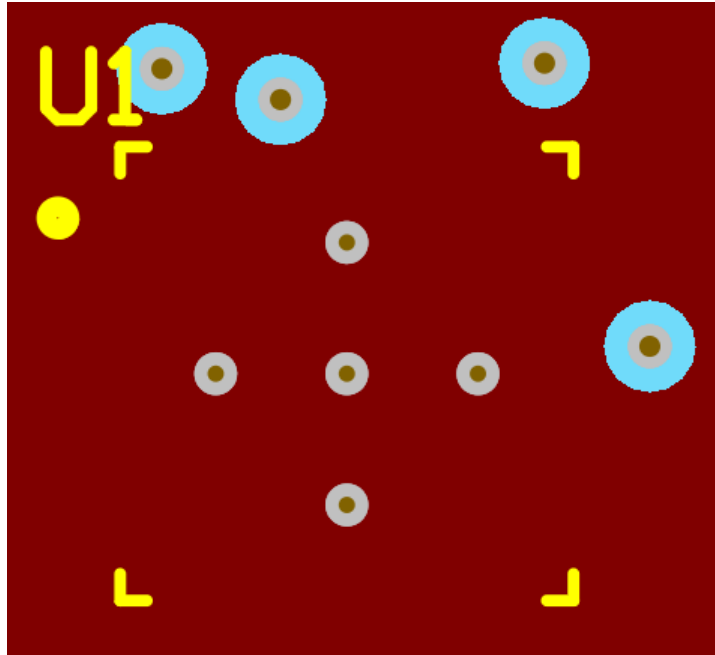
PCB Layout Example for CDCDB400, GND Layer
